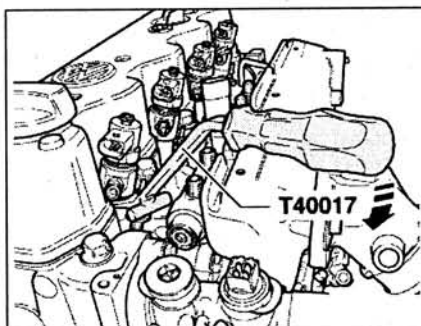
Вкрутите снова болт 4 крепления держателя в отверстие, установите рычаг Т40017 на опорный болт и извлеките форсунку.
